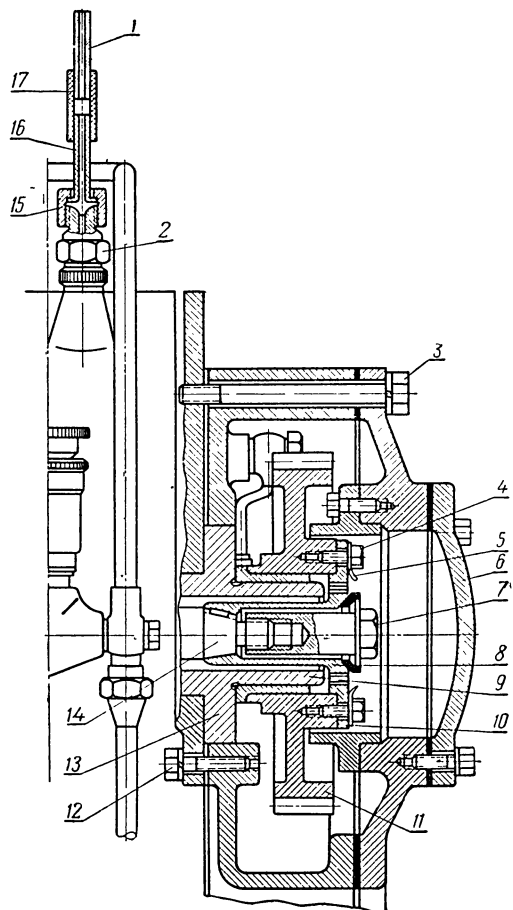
Топливный насос с приспособлением для проверки величины угла опережения подачи топлива:
